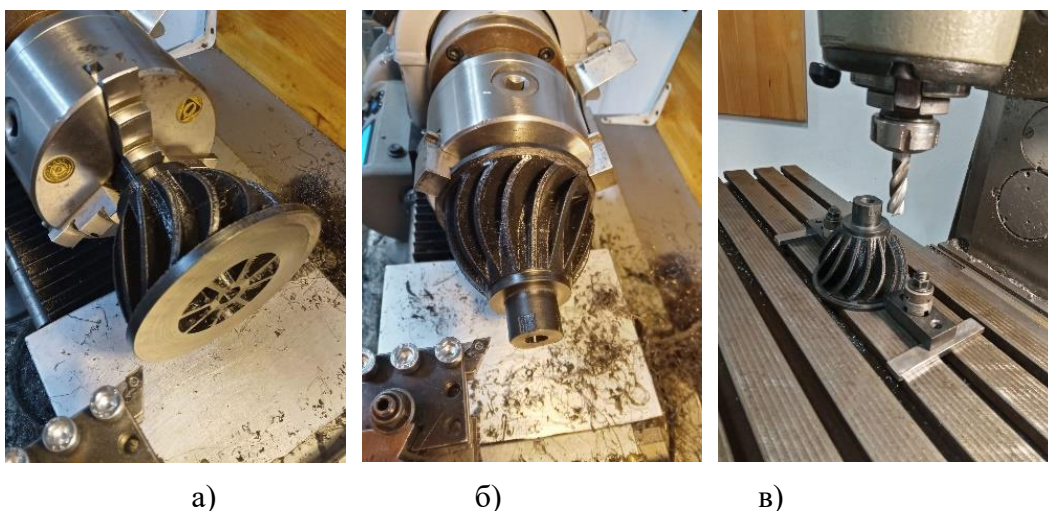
Процес механічної обробки. а), б) Точіння, в) Фрезерування
